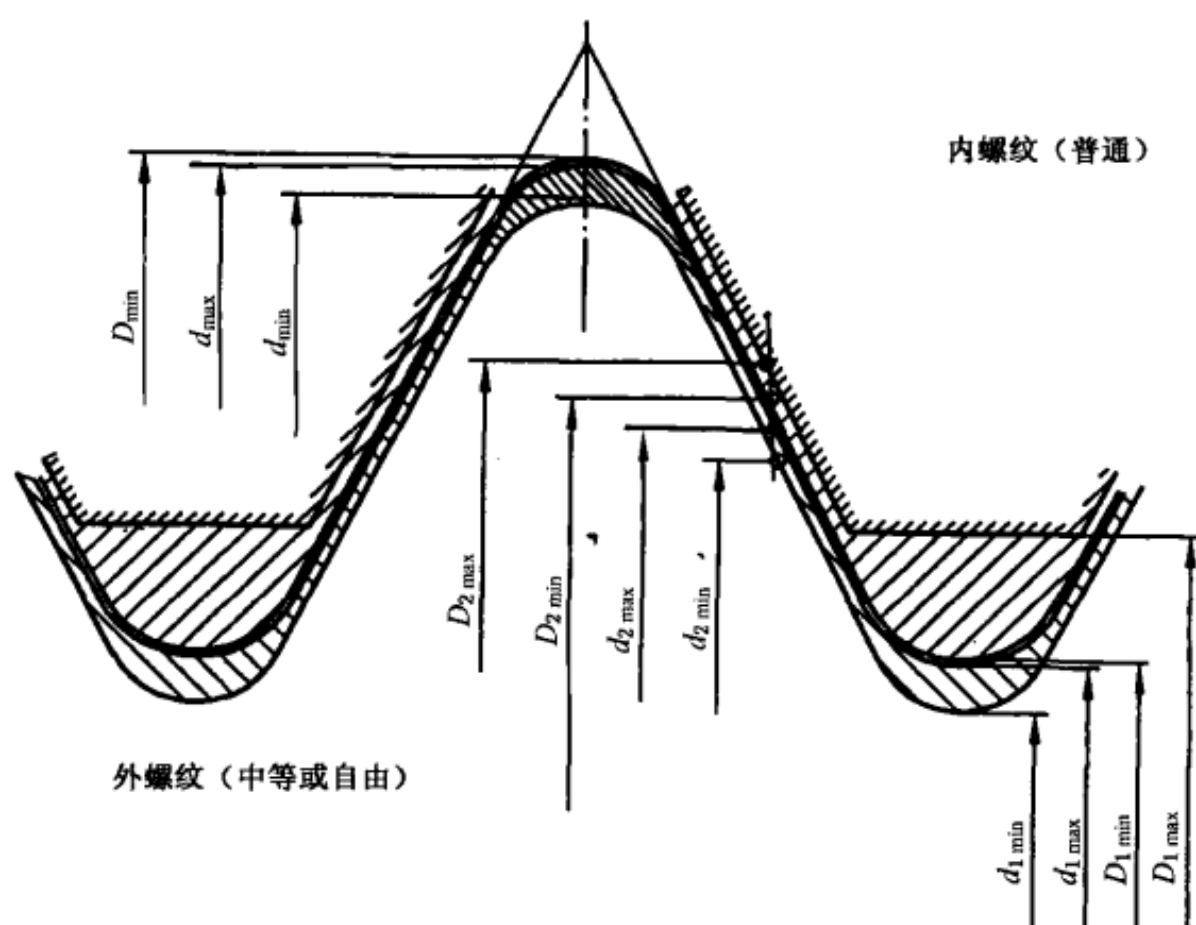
惠氏普通内螺纹与中等或自由外螺纹配合的公差带位置(公称直径小于或等于 3/4 in)
